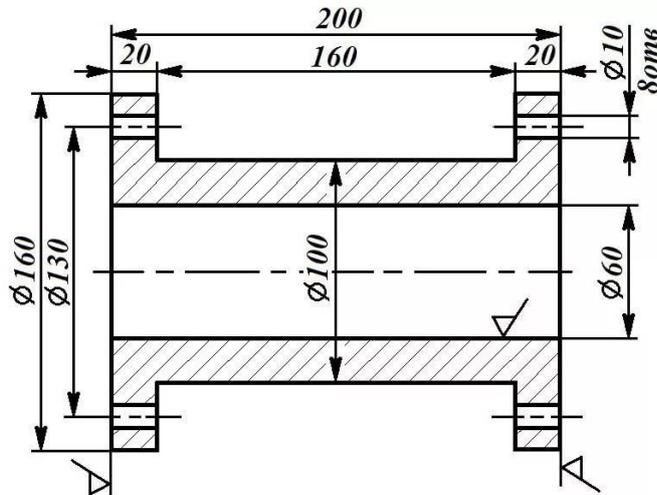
Эскиз детали «Патрубок», материал – сталь 40ХН.
